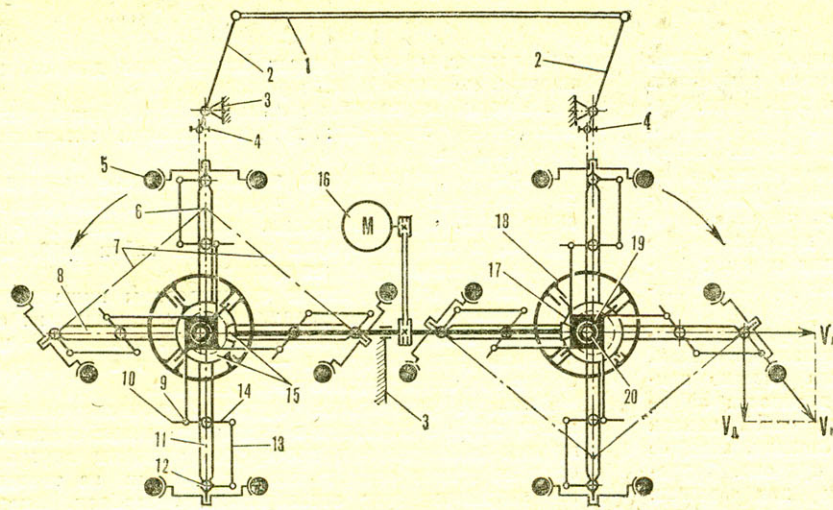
Принципиальная схема «танцующего» автомобиля: 1 — рулевой обруч, 2 — командные рычаги, 3 — корпус автомобиля, 4 — шаровые шарниры, 5 — колесо, 6 — общая точка осей противолежащих колес, 7 — линия осей колес, 8, 11 — лучи ротора, 9 — скользящий шарнир, 10 — стержень, 12 — шарнир поворота колеса, 13 — тяга, 14 — рычаг, 15 — пара конических шестерен, 16 — электродвигатель, 17 — ротор, 18 — крестовая муфта, 19 — крестовина, 20 — эксцентрик.
